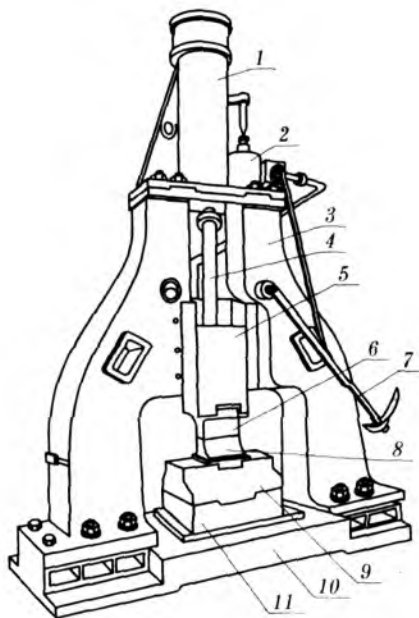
Паровоздушный ковочный молот арочного типа:
